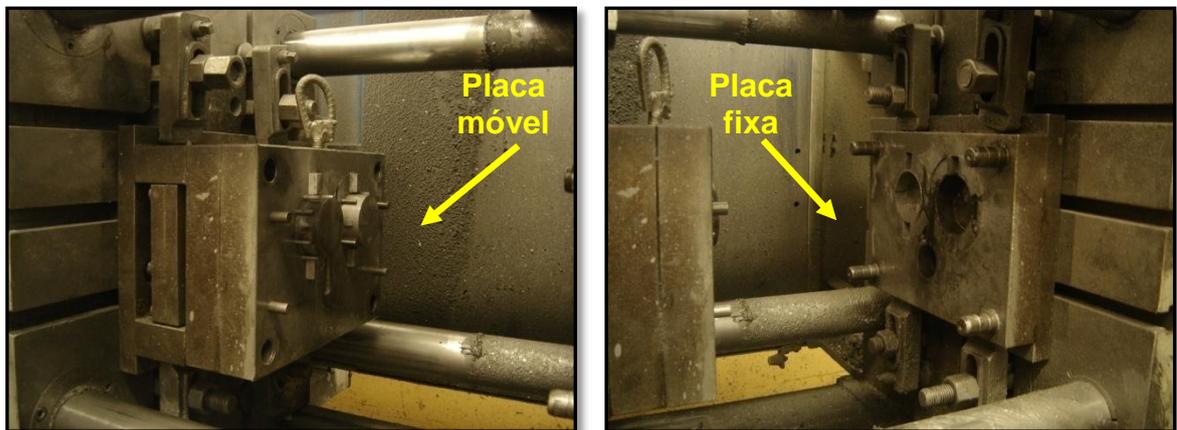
Molde já colocado na máquina injetora (Esq.: placa móvel; Dir.: placa fixa)
